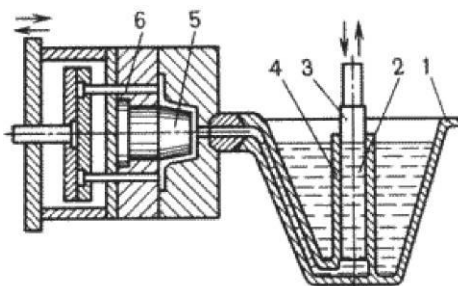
Схема изготовления отливки на машинах с горячей камерой прессования
